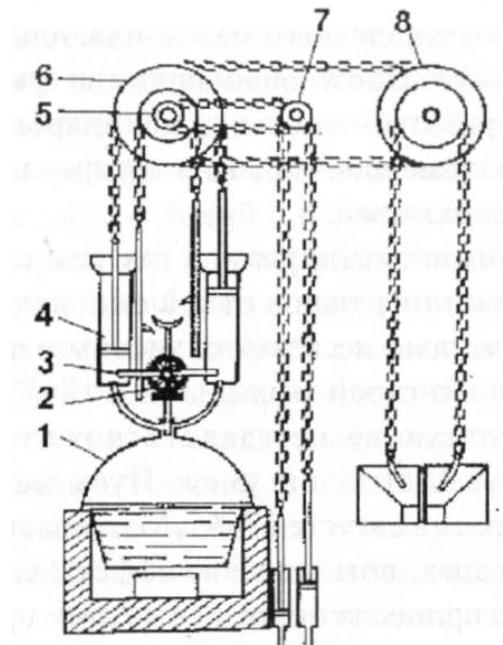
Схема универсального теплового двигателя И.И.Ползунова: 1-паровой котел; 2-автомат водопарораспределения; 3-трубопровод подачи охлаждающей воды; 4-левый цилиндр с поршнем; 5-шкив привода автомата водопаро-распределения; 6-шкив передачи движения поршней; 7-шкив привода питательного насоса парового котла; 8-шкив привода воздуходувки
